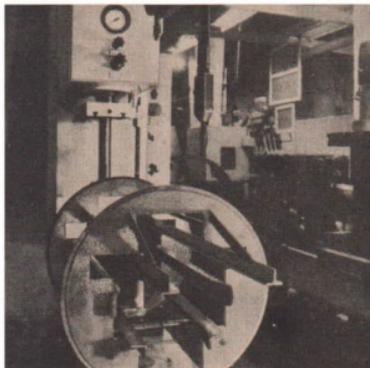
/2 Hydraulische Presse zum Ausdrücken der Zylindergleitbuchsen kombiniert mit einem Rhönrad
